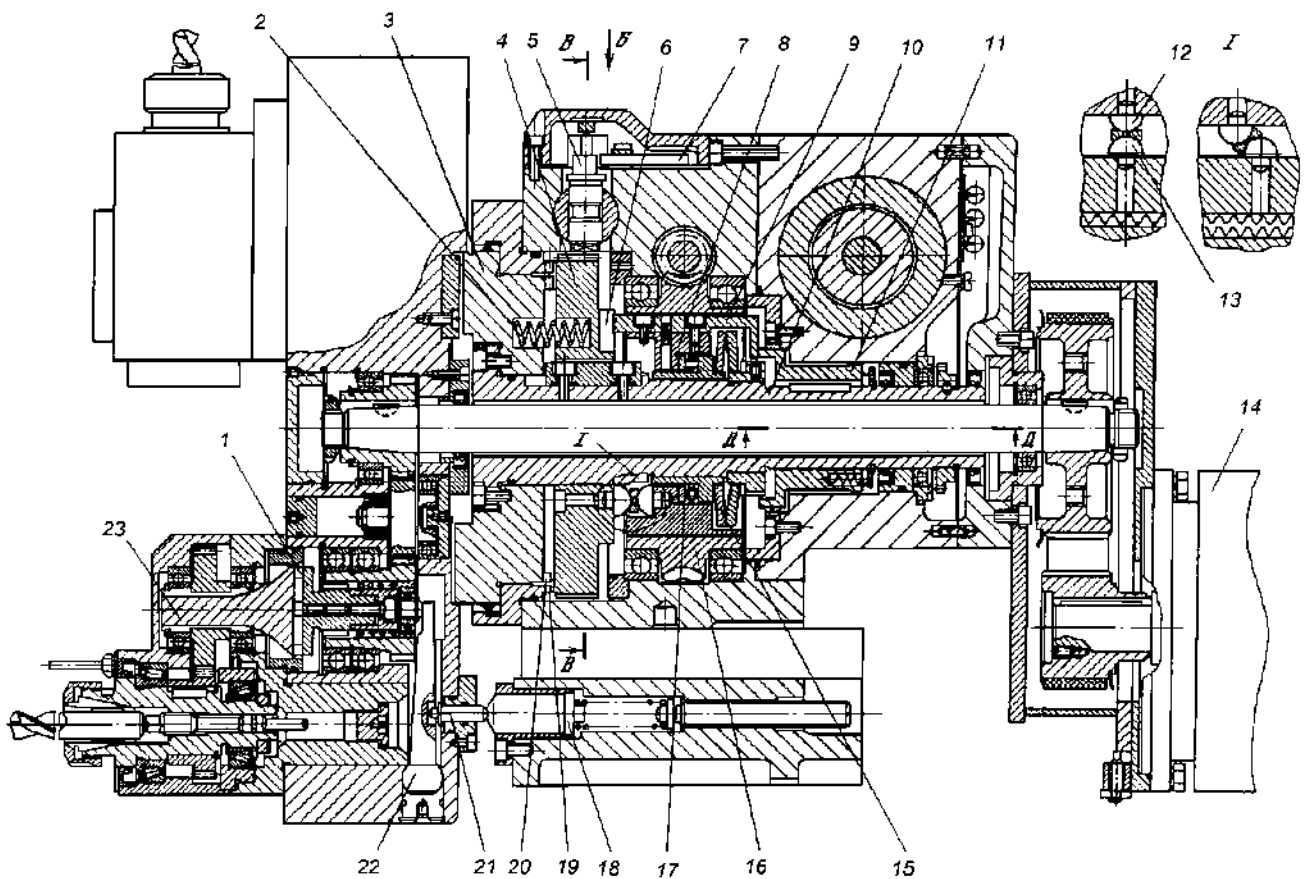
Револьверна головка багатоопераційного верстата
